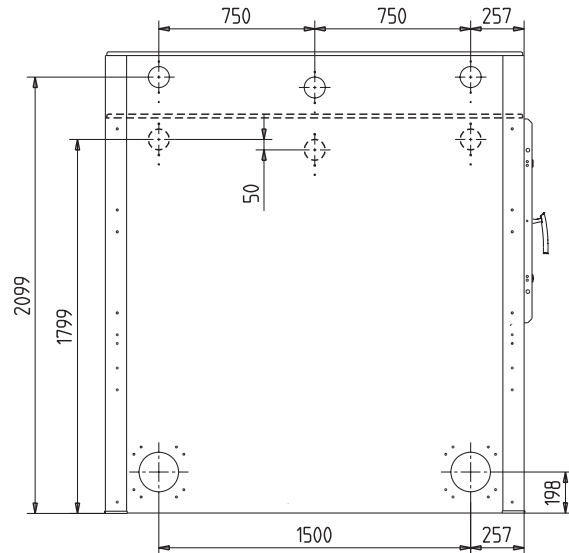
Stahlblech-Tanks mit Breite 2,0 m – Ansicht von links
